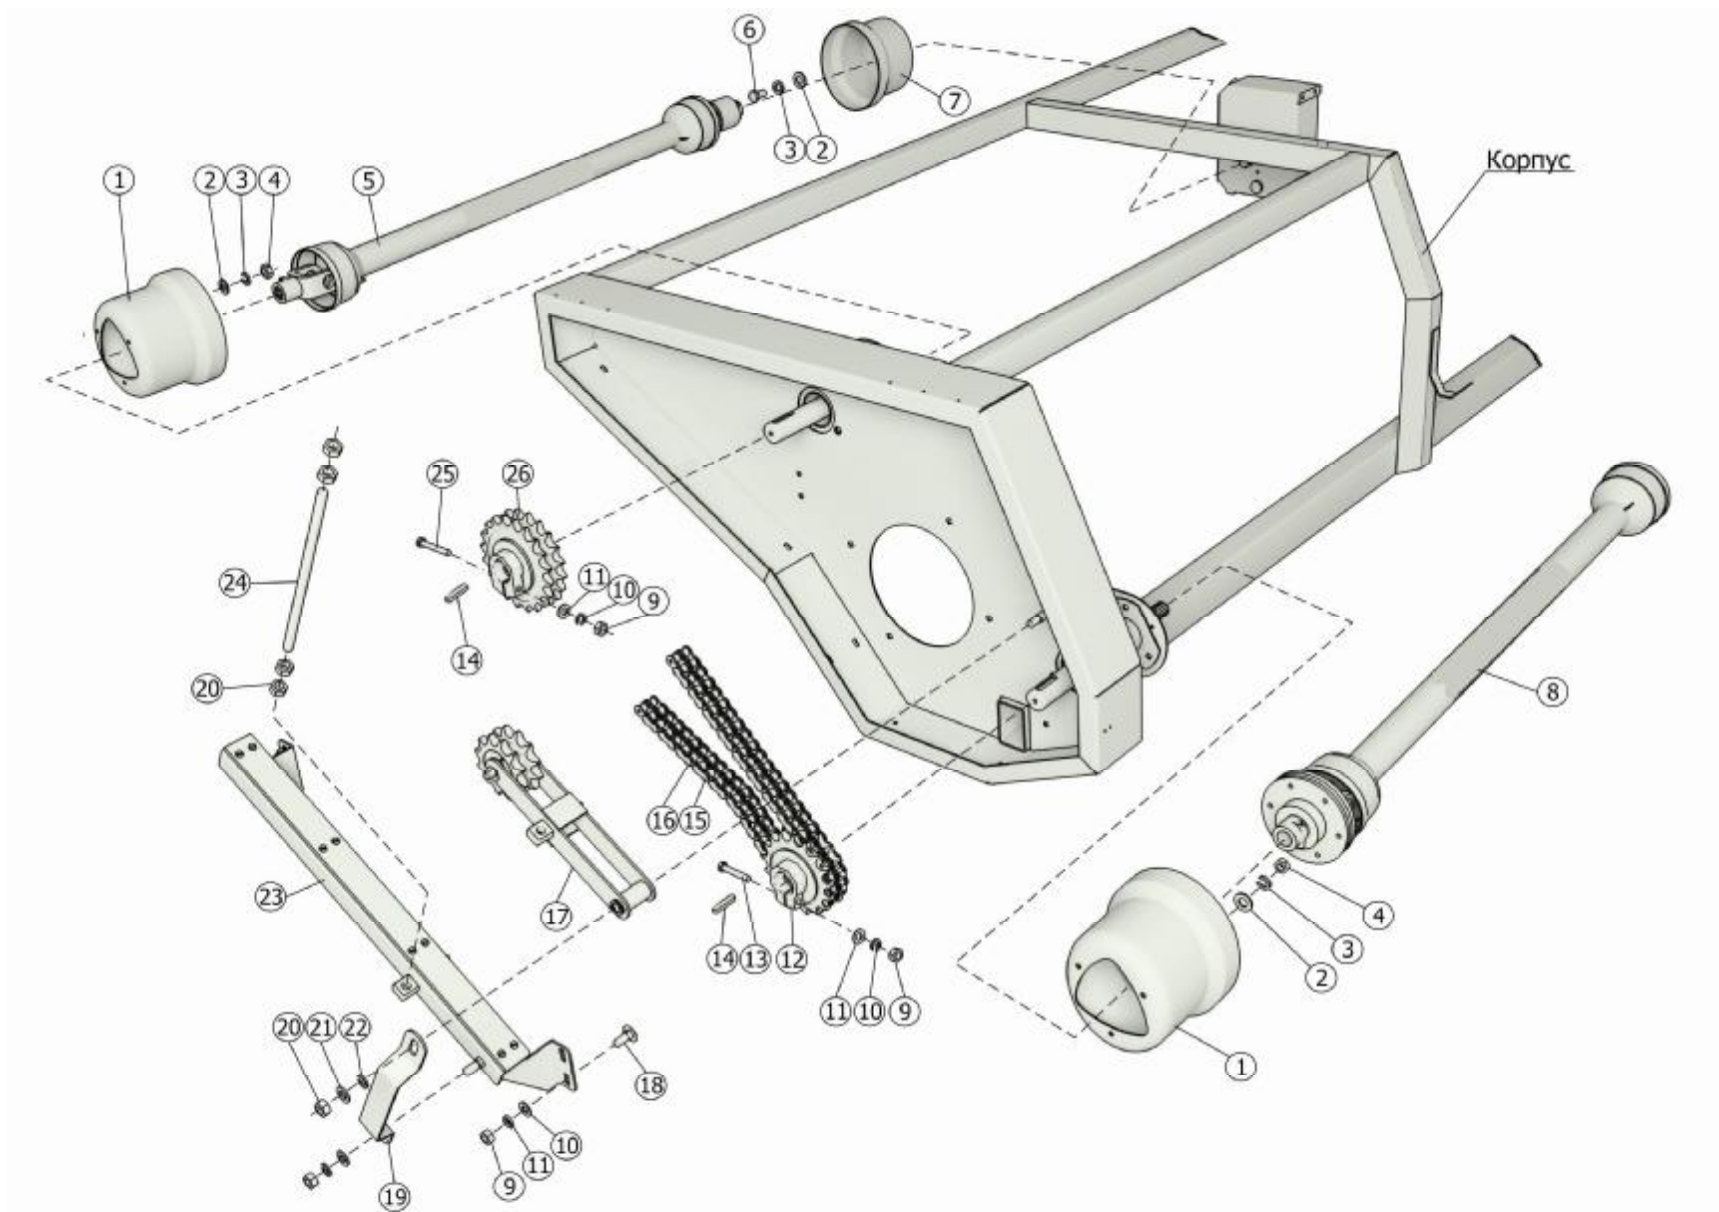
Установка приводов ЖРН-601.06.00.000. Левая сторона
